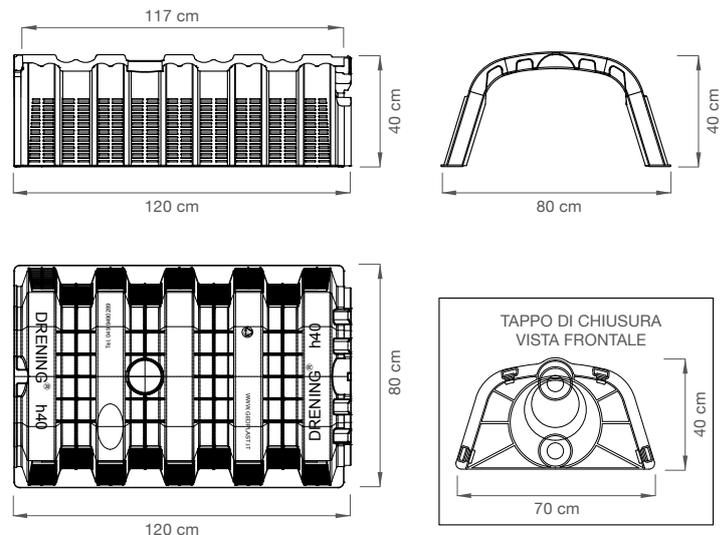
Disegni dimensionali DRENING e tappo di chiusura
